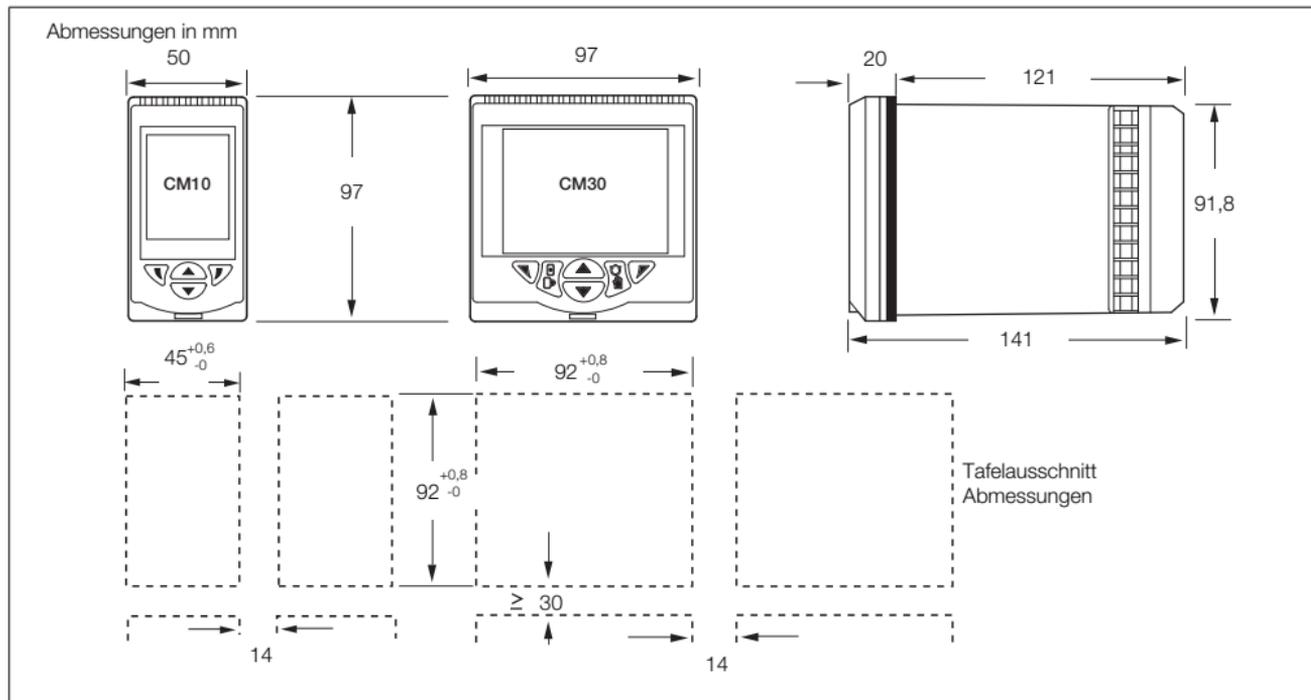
Abmessungen von ControlMaster CM10 und CM30
